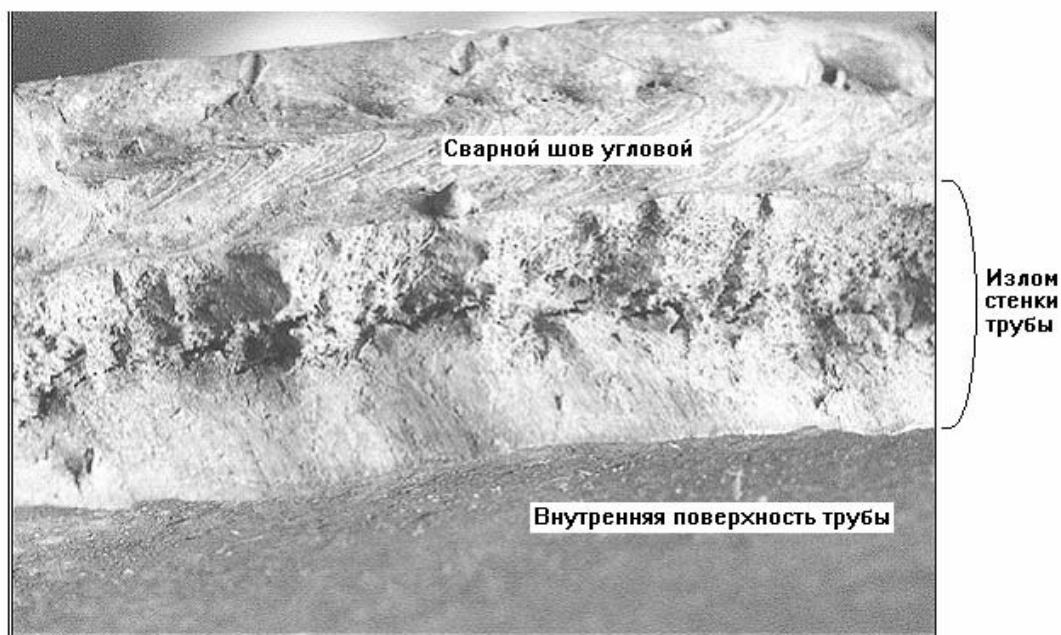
Излом стенки трубы по месту разрушения (сверху сварной шов “вантуз-труба”)
